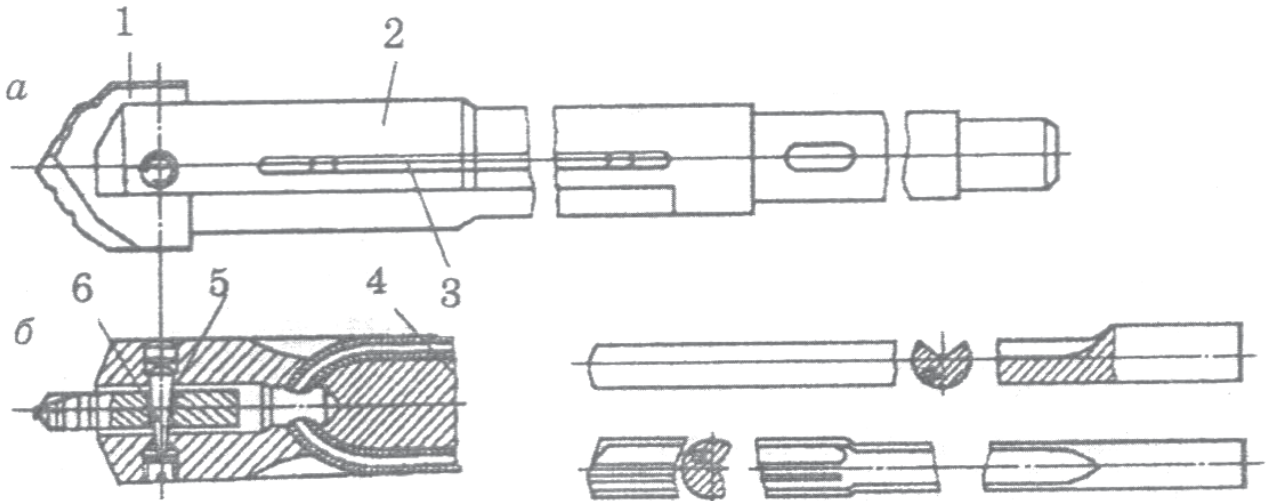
Сверла для глубокого сверления: 1 – режущая пластина; 2 – штанга; 3 – канавка; 4 – трубки; 5 – винт; 6 – клин
